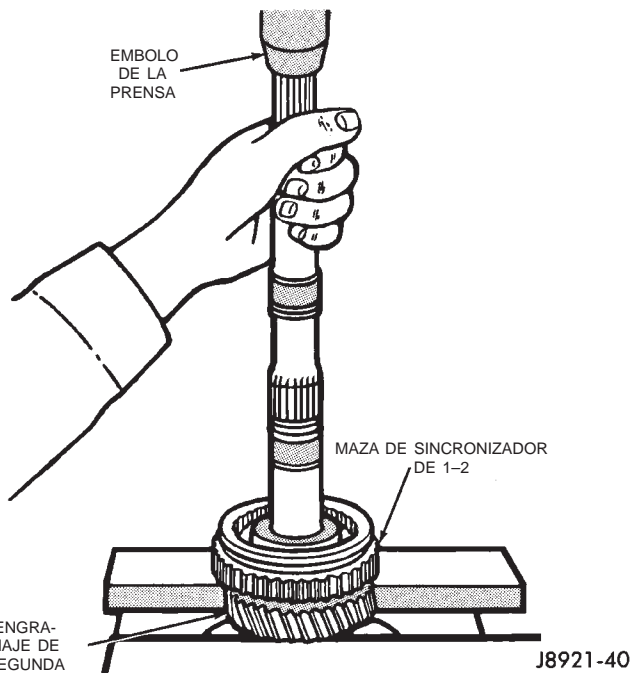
Desmontaje de engranaje de segunda velocidad, engranaje de marcha atrás y el sincronizador de 1-2
